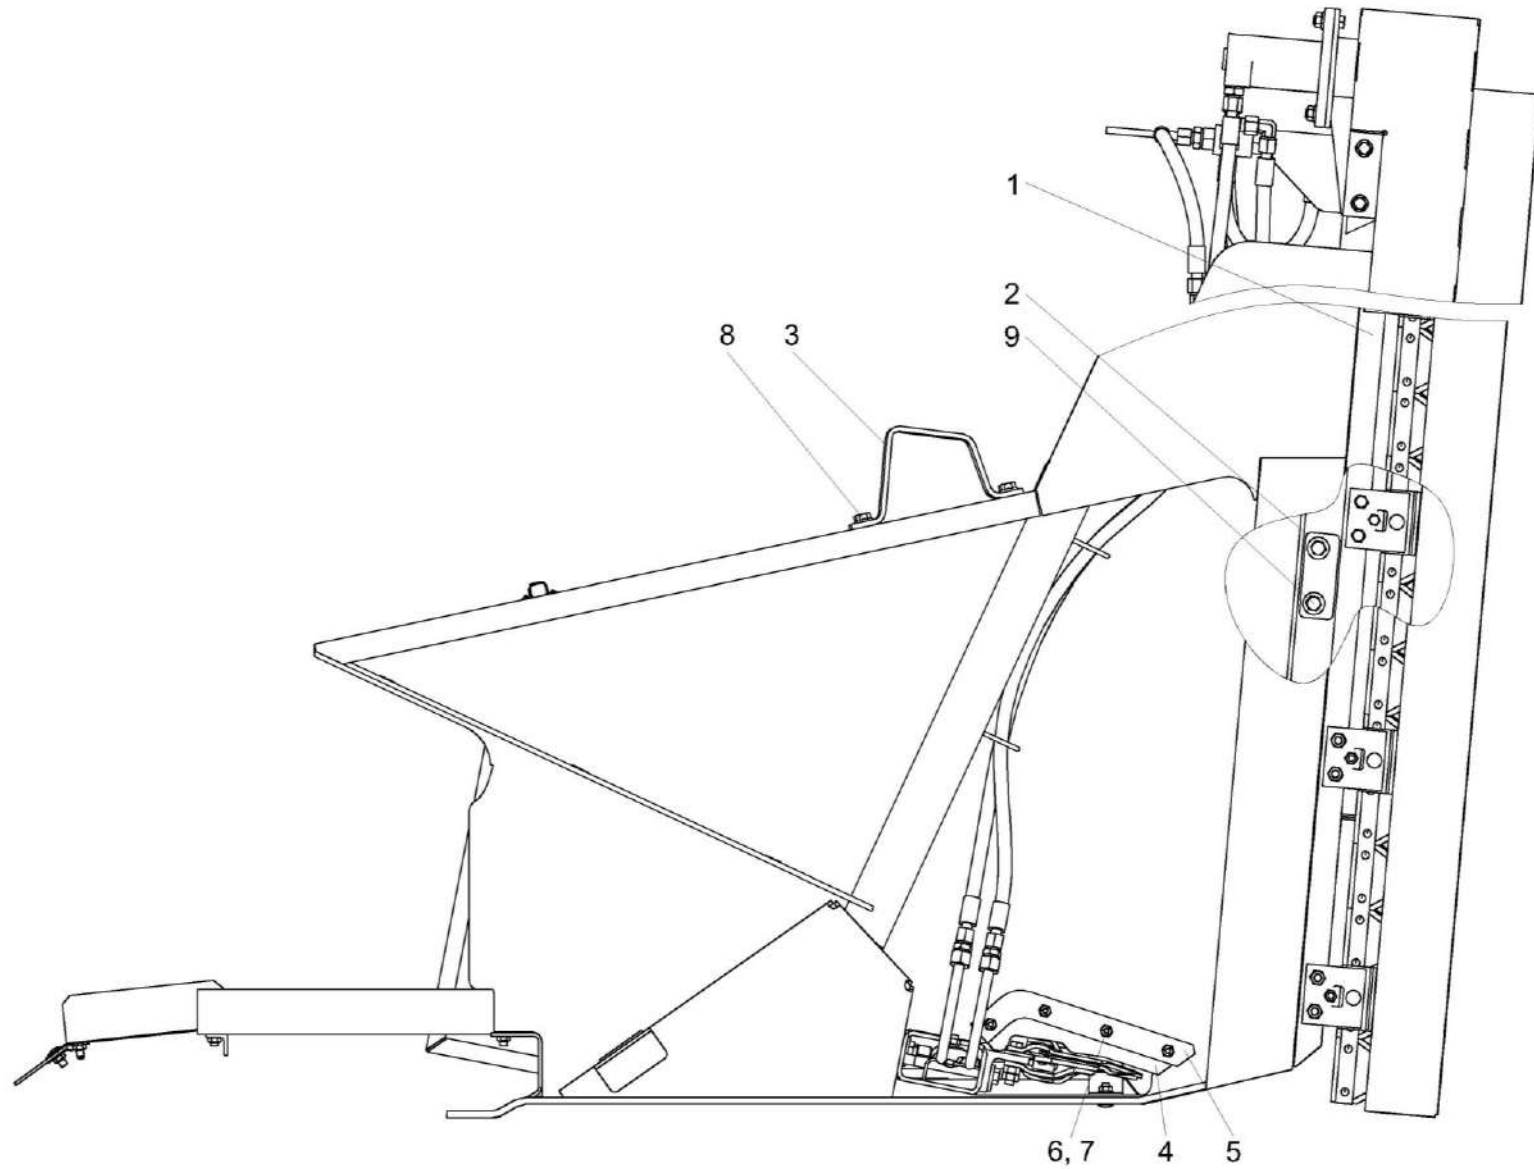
Приспособление для уборки рапса КЗК 2540000А (лист 3)
